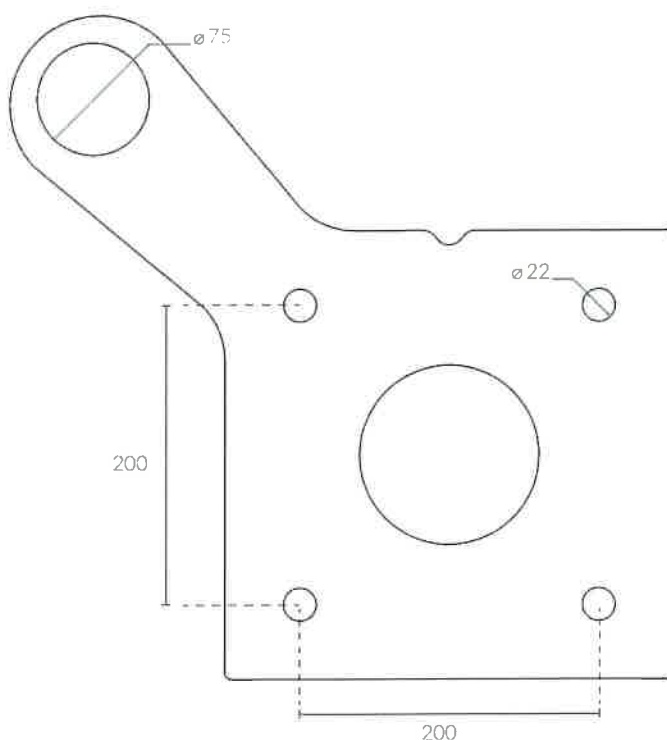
Esquema de furação para instalação do suporte inferior e poste de sinalização.
